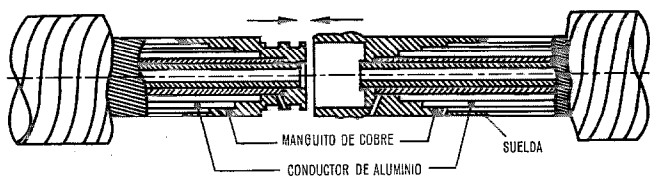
Empalme de conductores de aluminio mediante manguitos enchufables de cobre soldados y compresión hidráulica.
